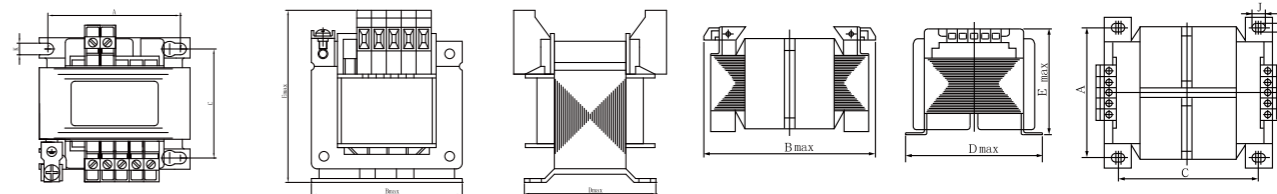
~800VA 系列变压器外形及安装尺寸图
